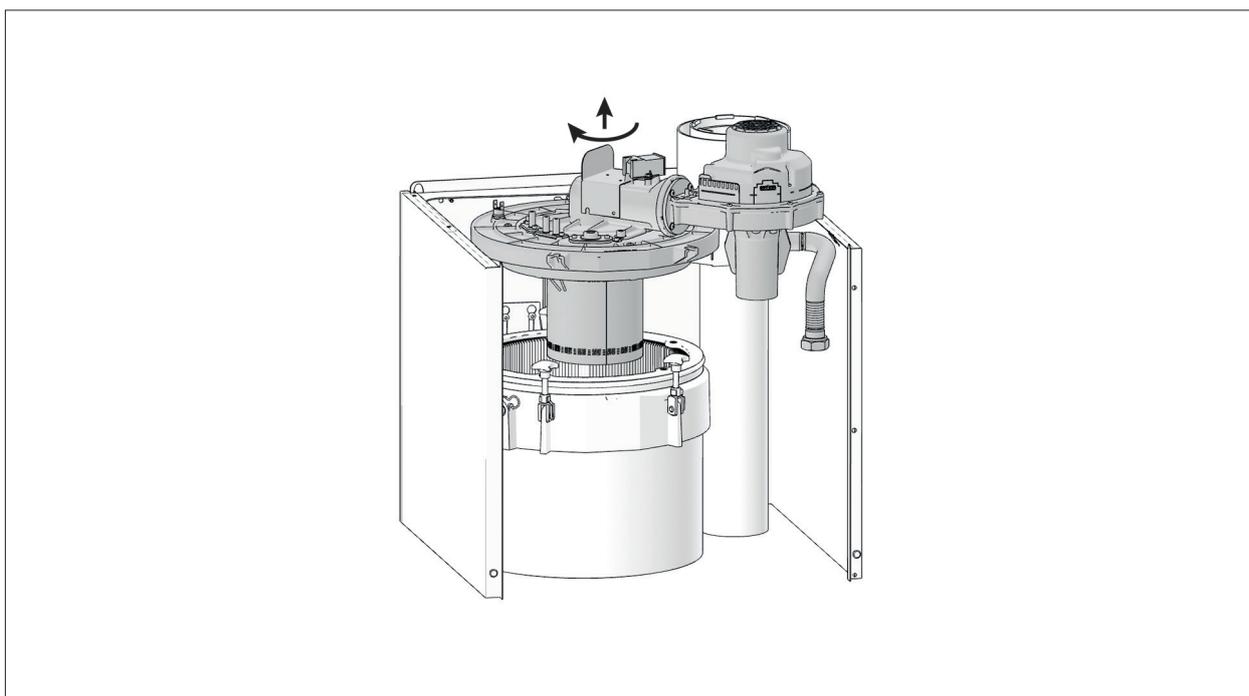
Soulever le couvercle de la chambre de combustion
